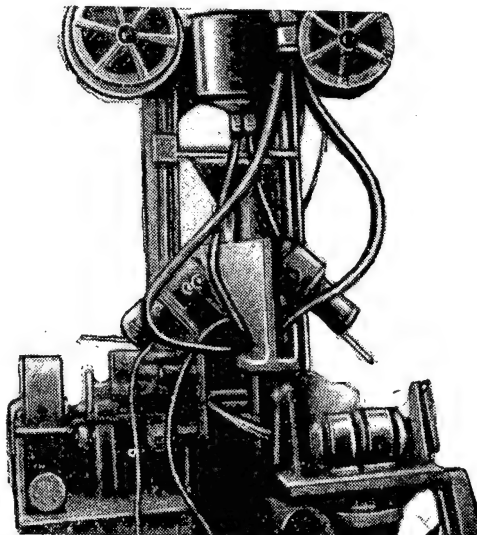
Станок для сборки и сварки тавровых балок
